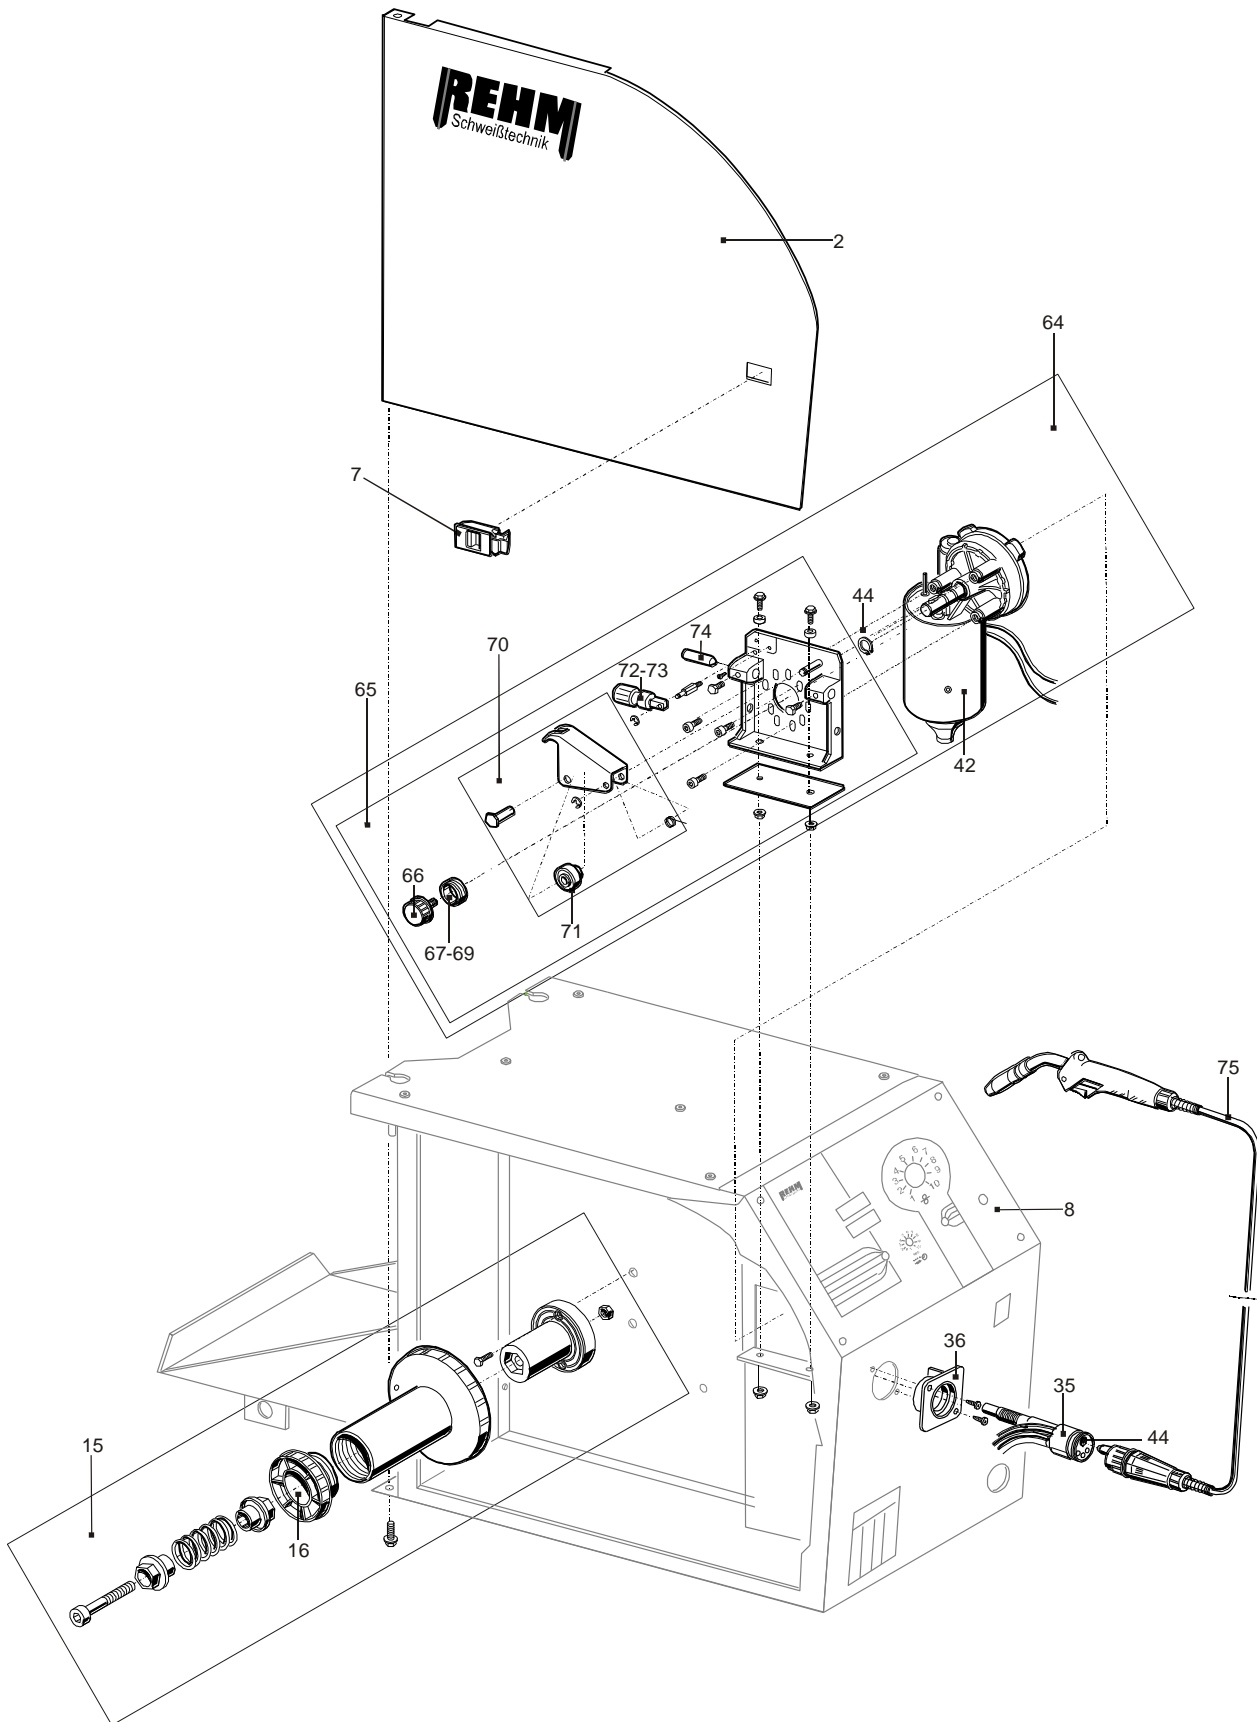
Explosionszeichnung SYNERGIC.PRO² 170-2 – 310-4 (links)
